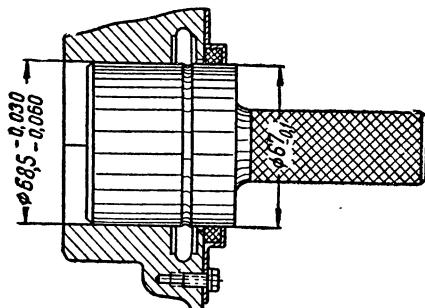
Оправка для запрессовки набивки сальника подшипника
